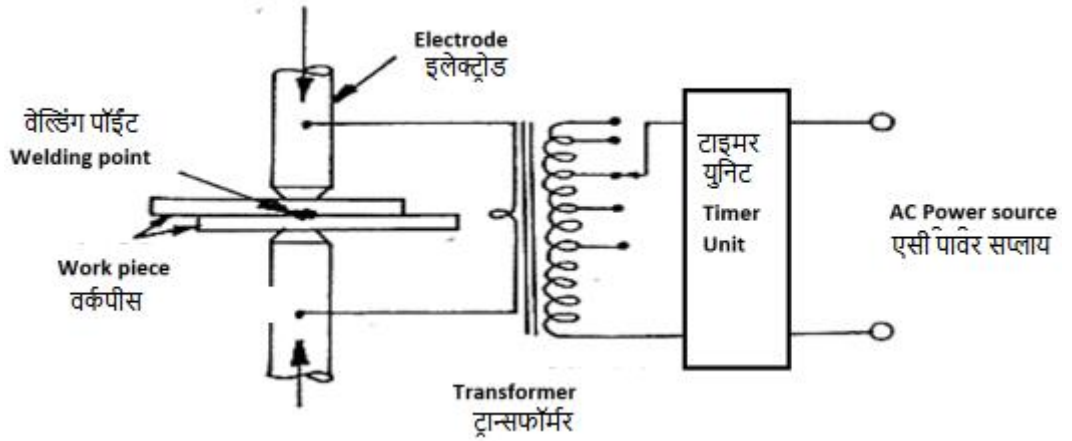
स्पॉट वेल्डिंग (Spot Welding)
